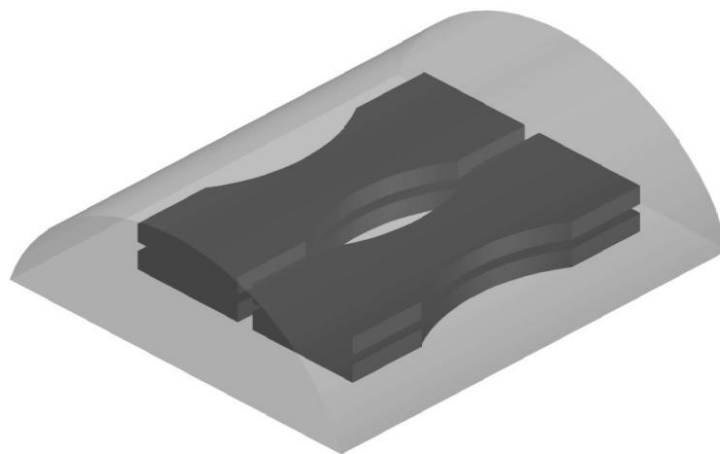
Zkušební těleso pro zkoušku únavy, Small Fatigue Test [68]
